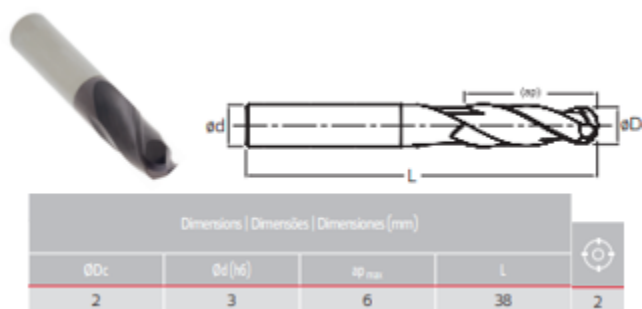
Fresa de bola diámetro 2 mm. Fuente [9]
